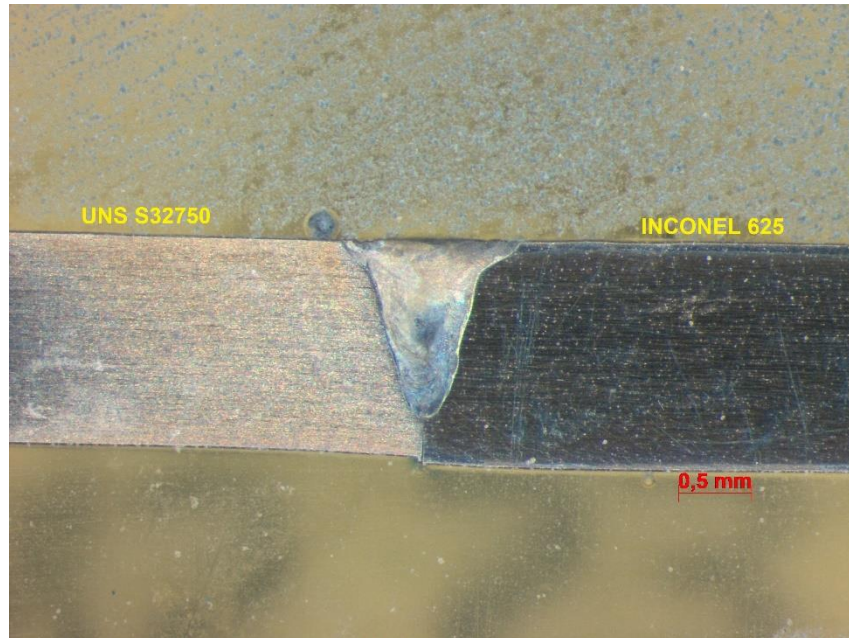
Corpo de prova 3, soldado com frequência 4,5 hz
